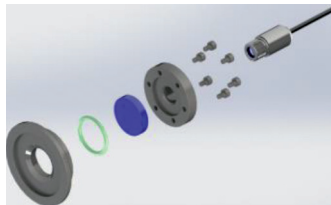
KF40 Flansch (TM-KF40GE-CT);
